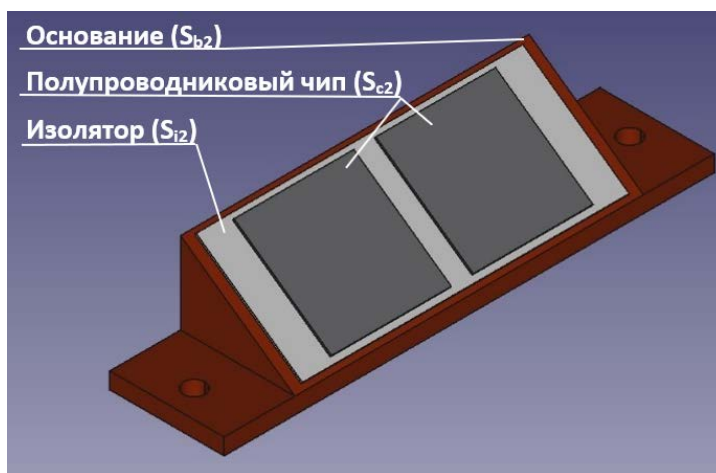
3D модель силового диодного модуля без корпуса с новой конструкцией основания.
